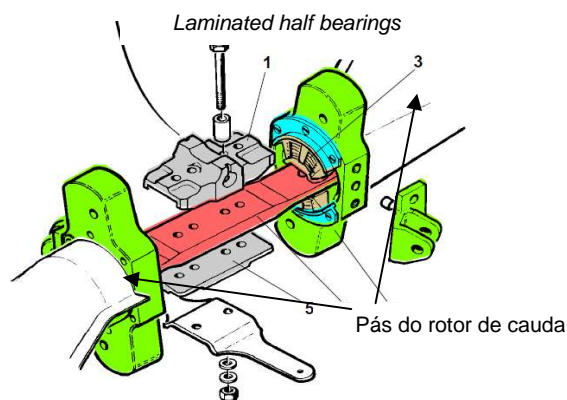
Montagem dos *laminated half bearings* em conjunto com as pás (lâminas) do rotor de cauda
